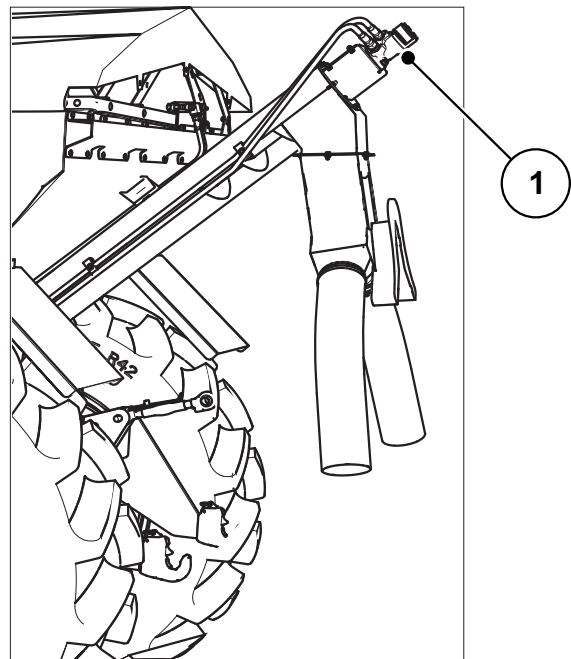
Cylinder hydrauliczny plandeki do przykrywania – przód
